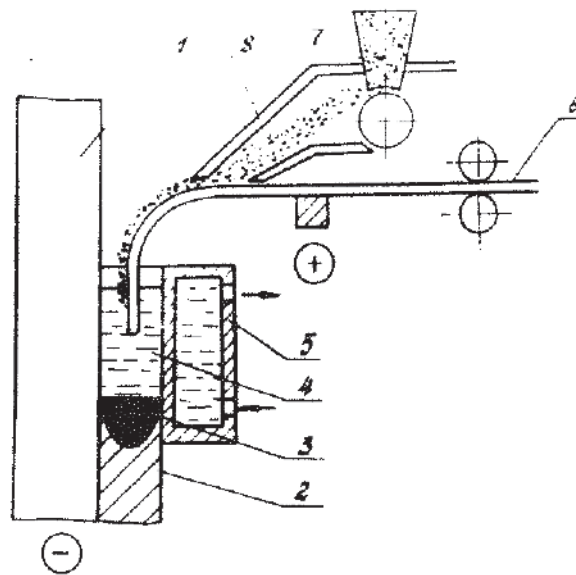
Схема электрошлаковой наплавки ферромагнитными порошковыми материалами /58/ :
